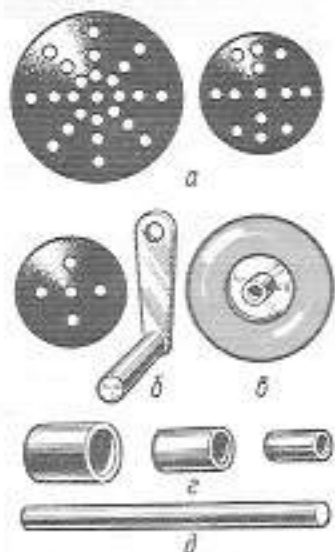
Дополнительные детали конструктора: а — шайбы; б — ручка; в — колесо; г — втулки; д — ось.
